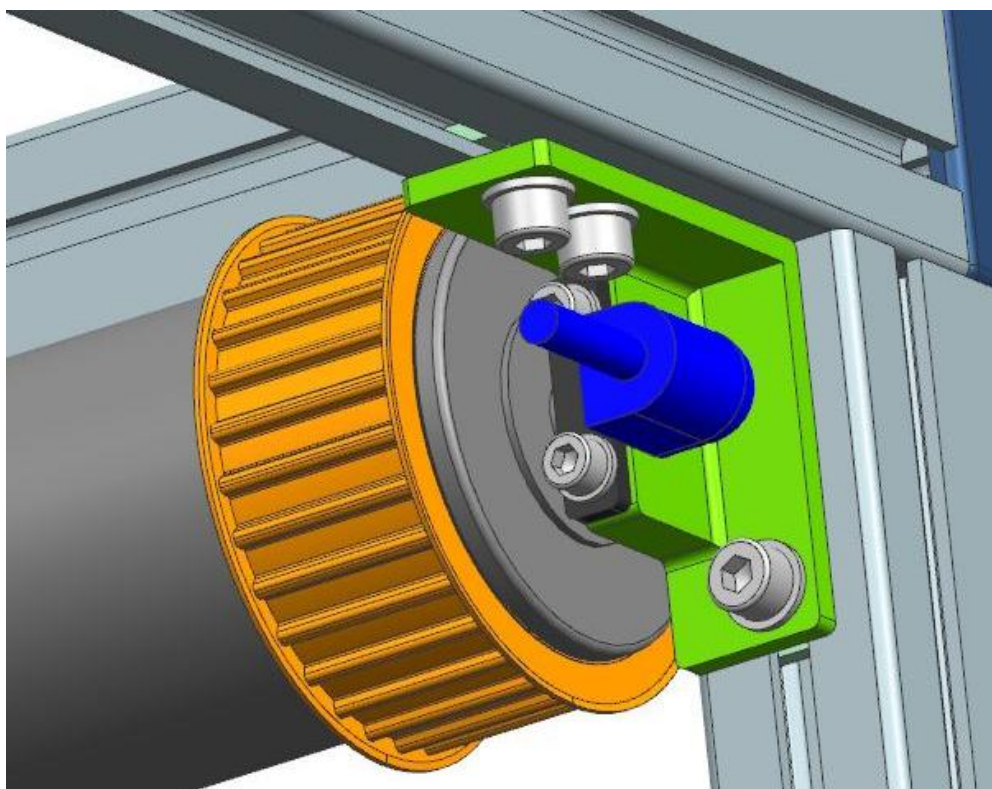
Bubnový motor s hnacími ozubenými řemenicemi
